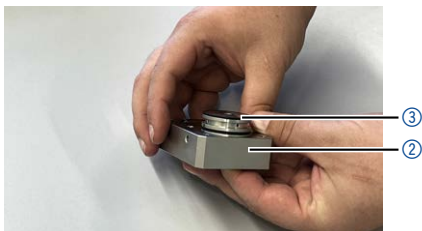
Entfernen der Einsatzbuchsen von der Druckplatte
